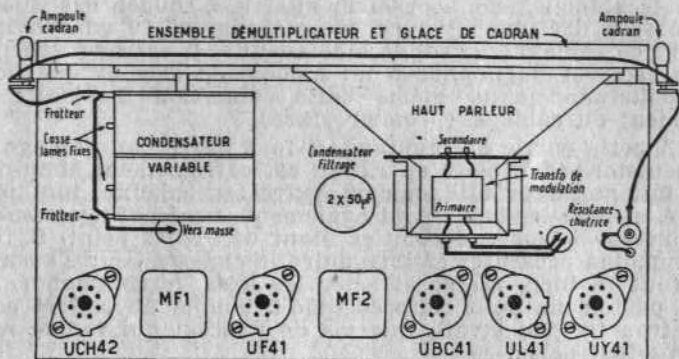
Montage mécanique du « MENUET » châssis vu du dessus
